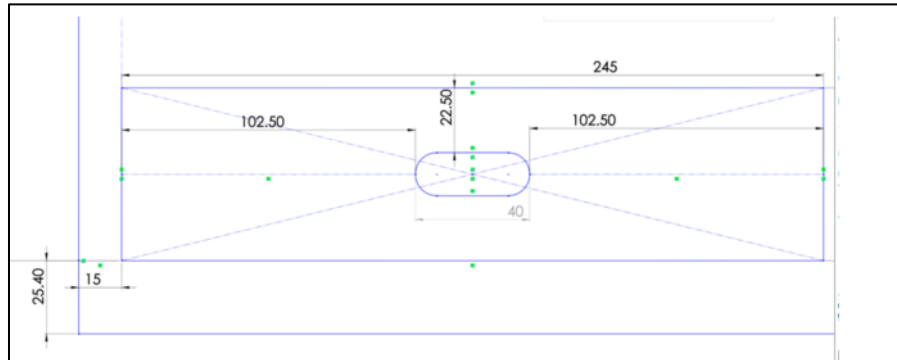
Centrado de barreno en un área de 245mm X 60 mm por una separación de 25.40mm X 15 mm.
